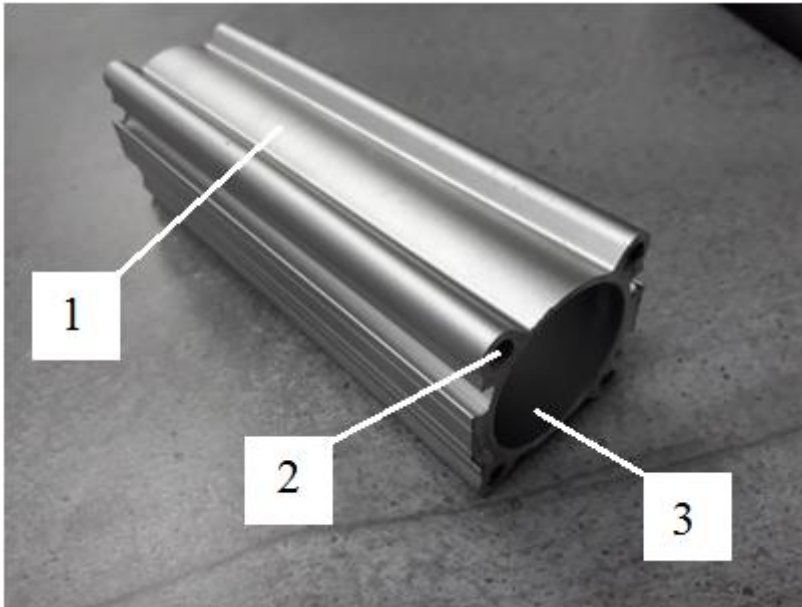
Загальний вигляд корпус пневмомолота.
